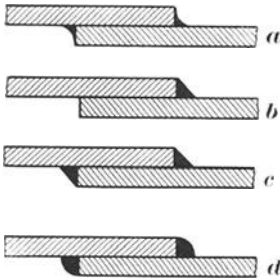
Ausführung der überlappten Schweißung.
